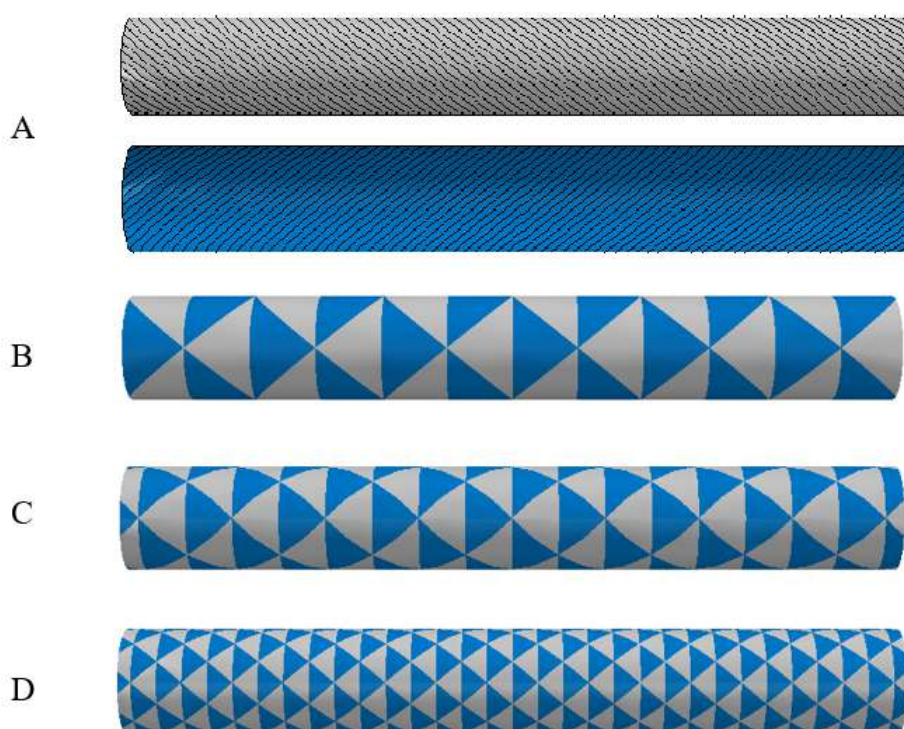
Disposição dos padrões de bobinagem no mandril de fabricação.
